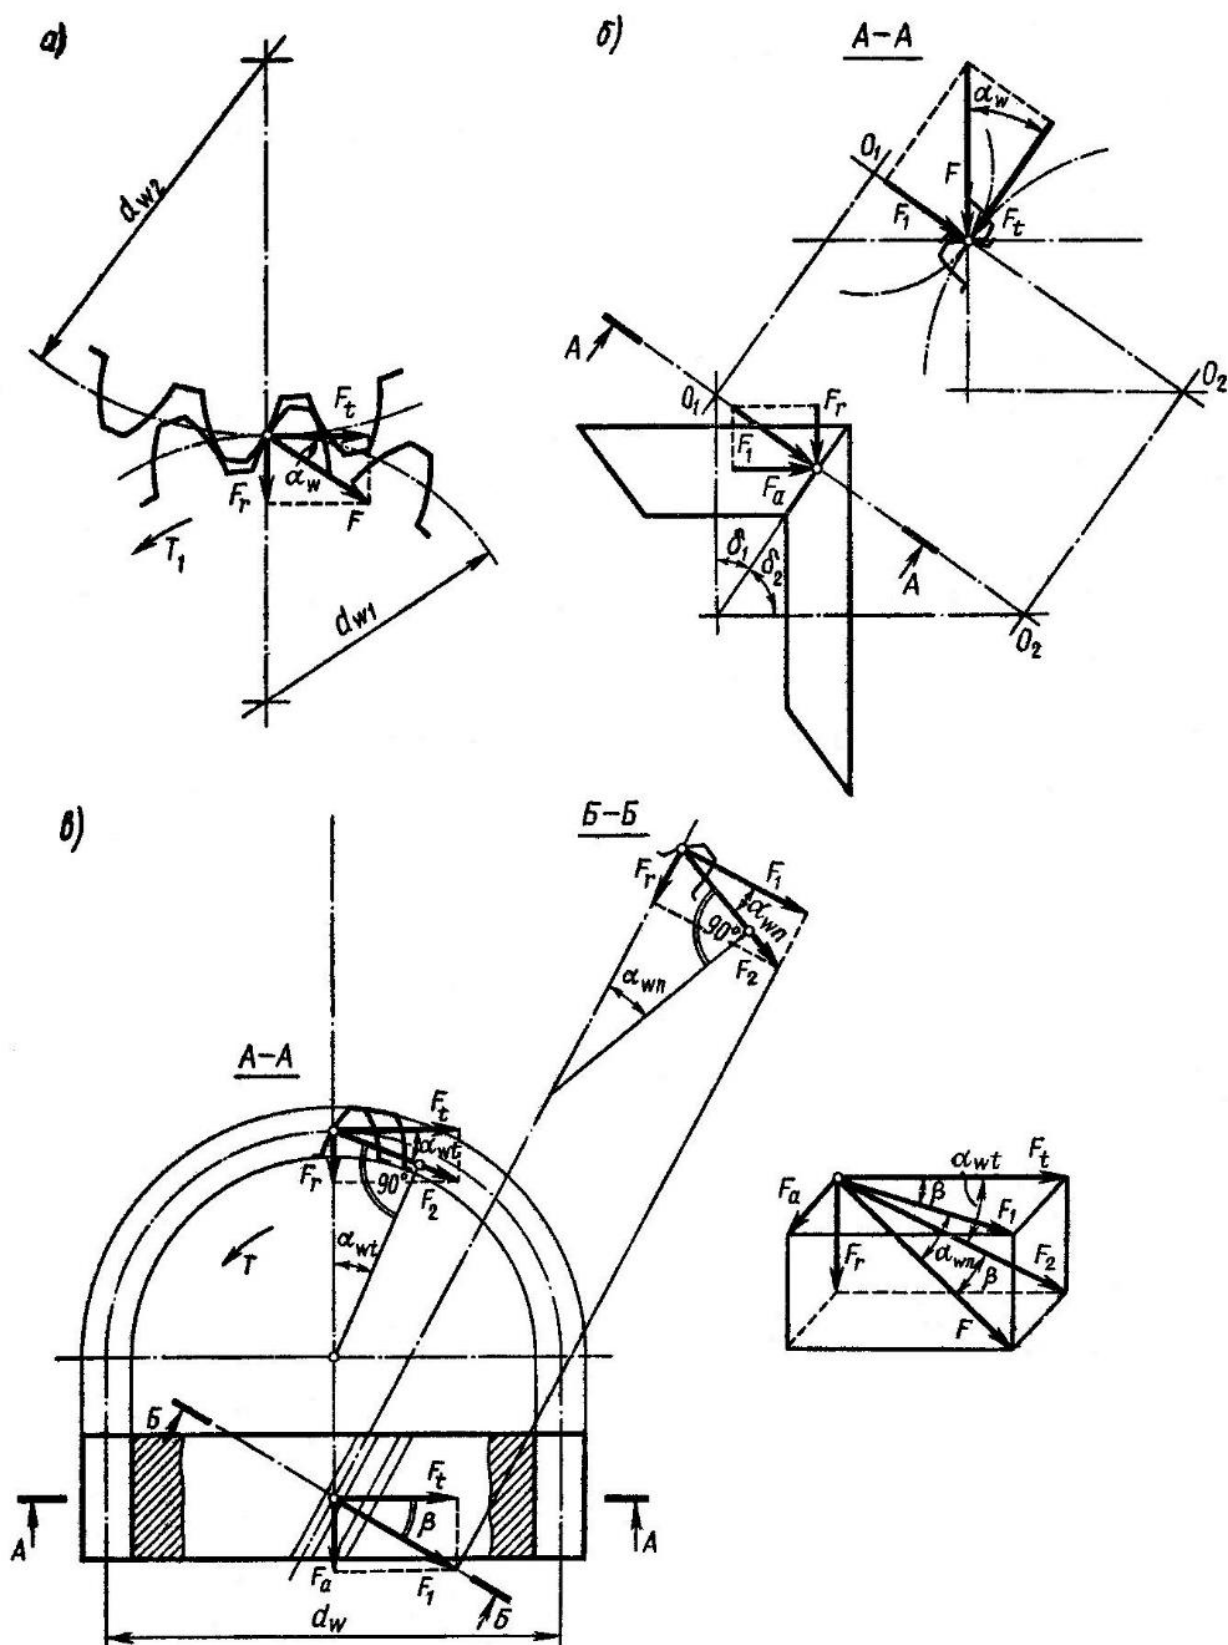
Схемы сил, действующих в зацеплении зубчатых передач
